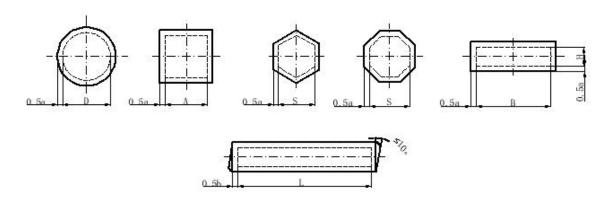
钛合金光轴类锻件机械加工余量与公差
